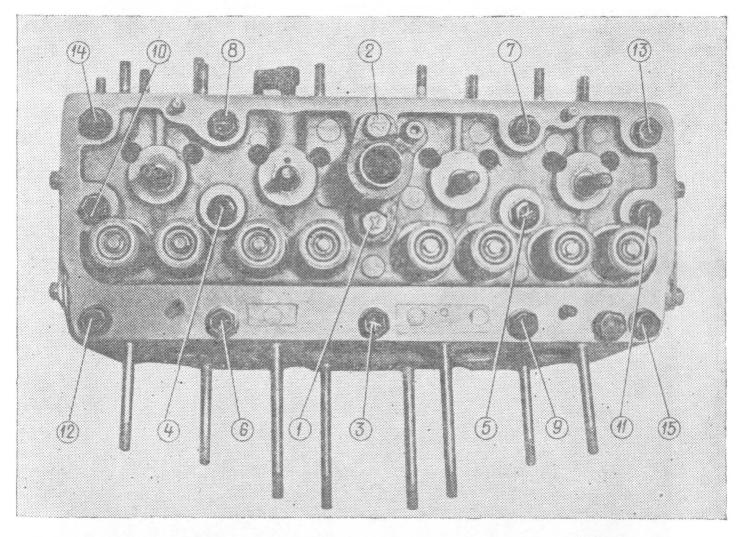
Anziehfolge für Muttern an Stiftschrauben zur Befestigung des Zylinderkopfes am Zylinderblock.
